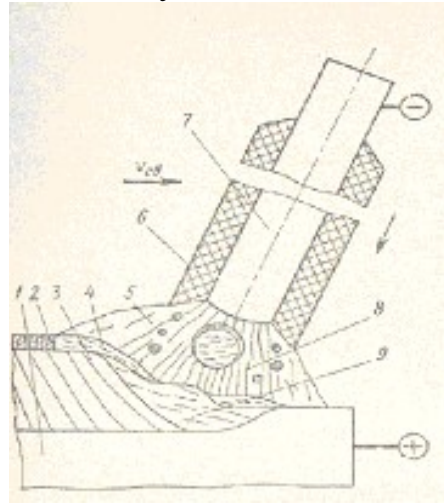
Схема процесса сварки металлическим покрытым электродом
